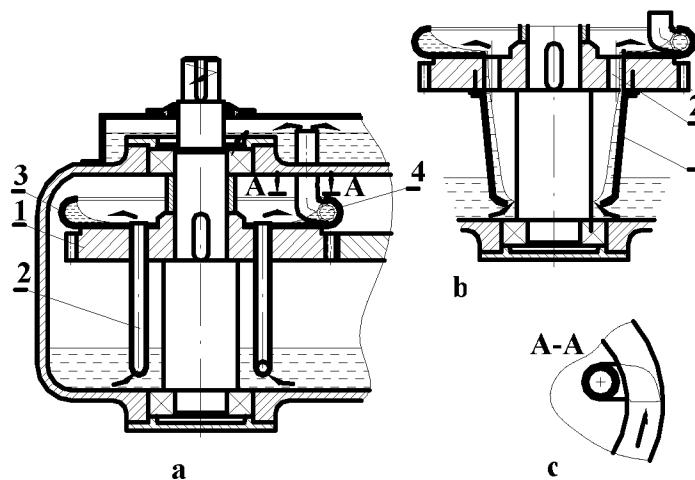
Принципиальная схема двухступенчатого способа смазки зубчатой передачи
